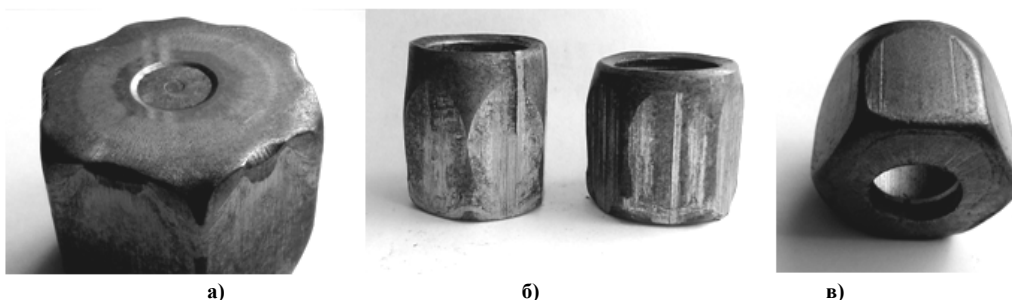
Поверхневі недоліки заготовки гайки отриманої холодним видавлюванням:
